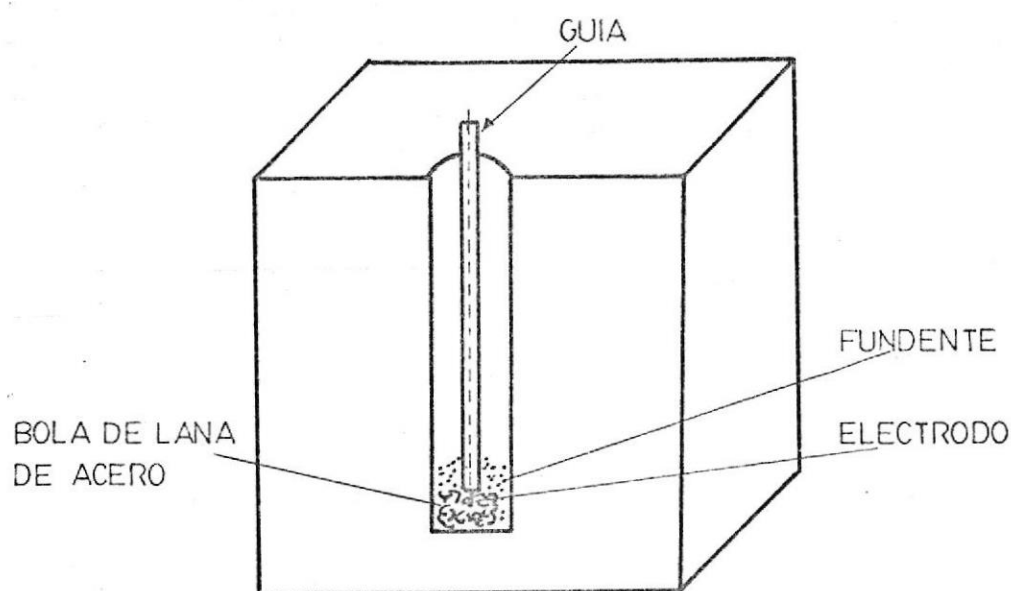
Representación del arreglo realizado para efectuar la soldadura por ESW.
